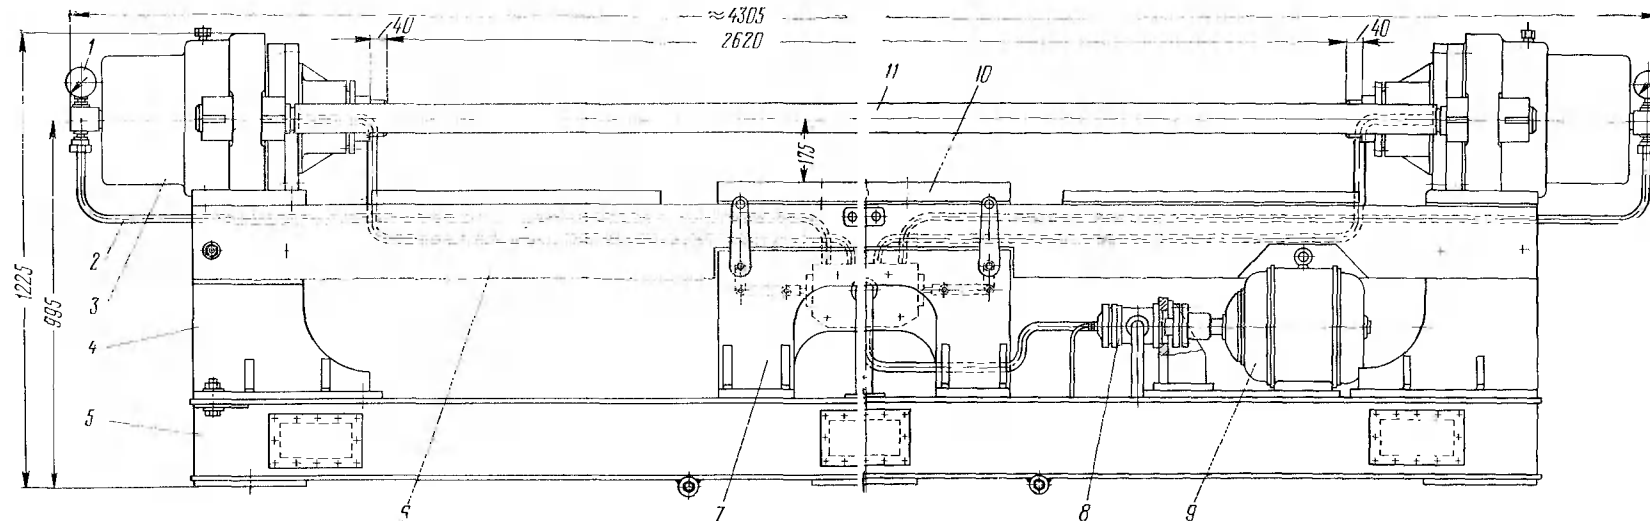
Пресс для перепрессовки кожухов полуосей заднего моста:
